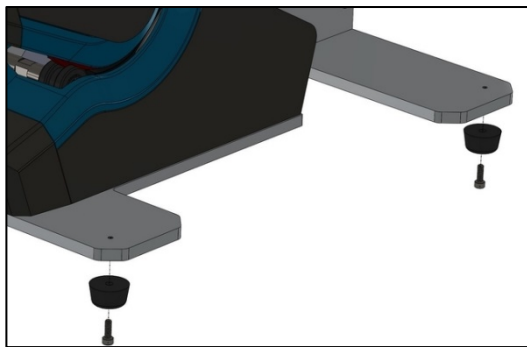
Entfernen oder befestigen Sie die vier Gummifüße mit einem 3mm-Inbusschlüssel. (zwei von vier dargestellt)
